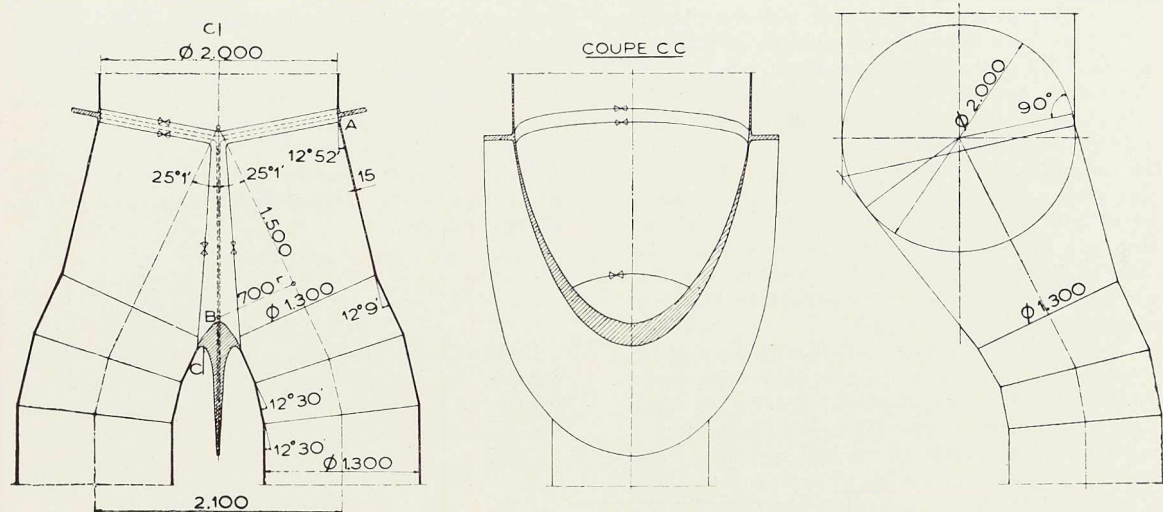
Dessin-projet d'un tuyau-raccord à deux branches.
